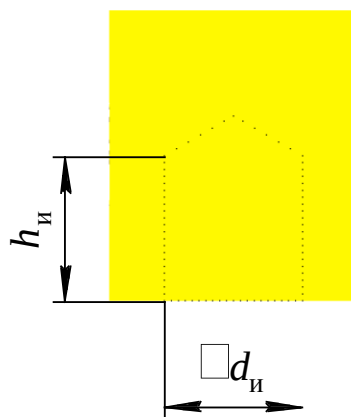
Точки, нанесенные на осевую плоскость заготовки, имитирующие исходную форму и размеры рабочей вставки
